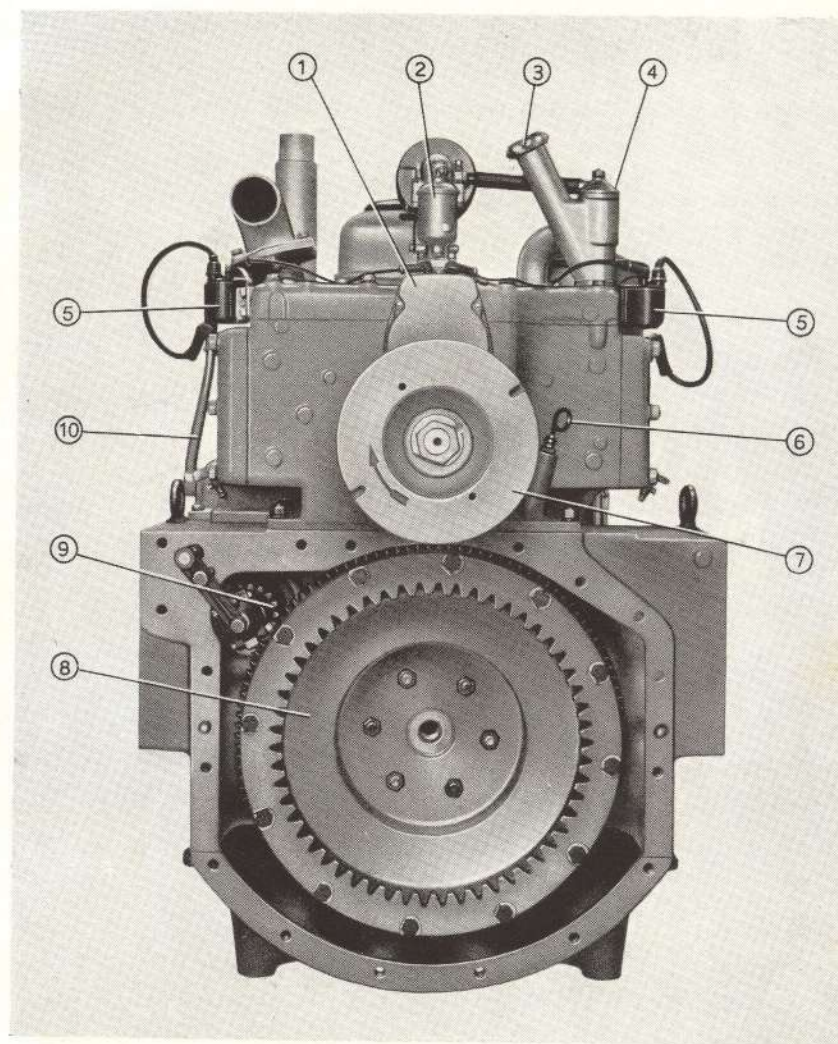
Vue arrière du moteur Diesel, avec moteur de lancement à essence.
